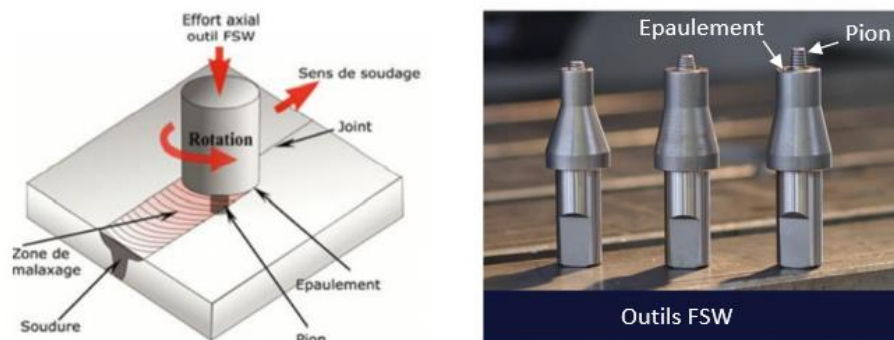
Principe du soudage par friction malaxage et outils FSW
